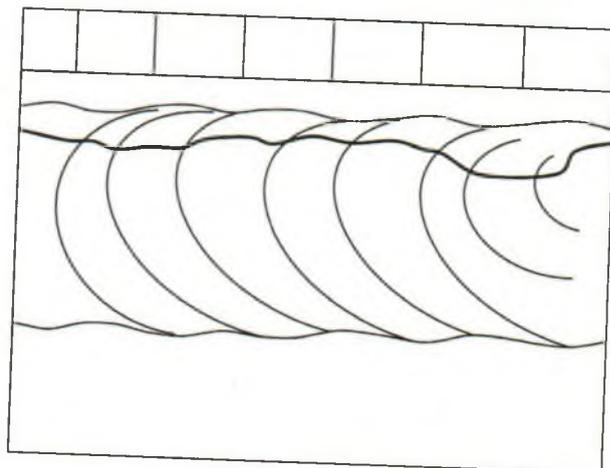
Продольная трещина таврового сварного соединения коробчатой конструкции подъемного сооружения на фоне поверхности с лакокрасочным покрытием
